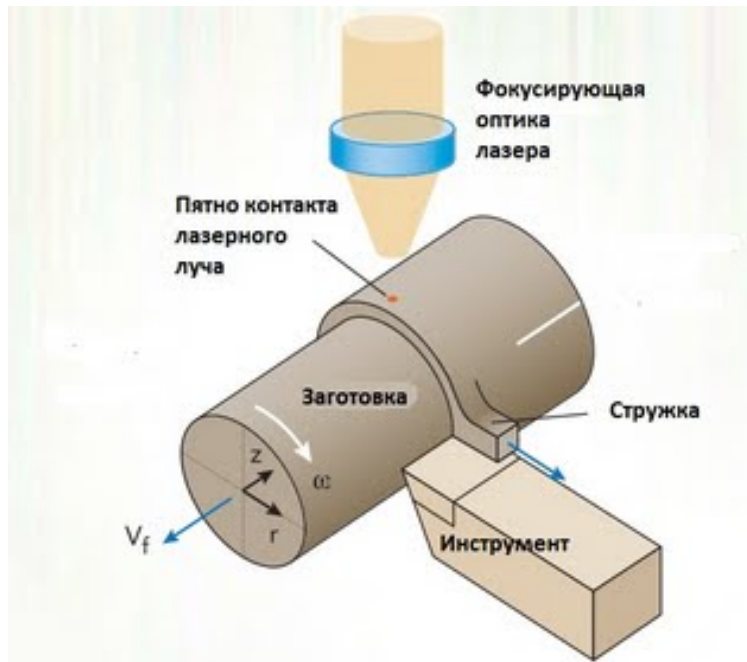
Схема механічної обробки з лазерним нагрівом.
